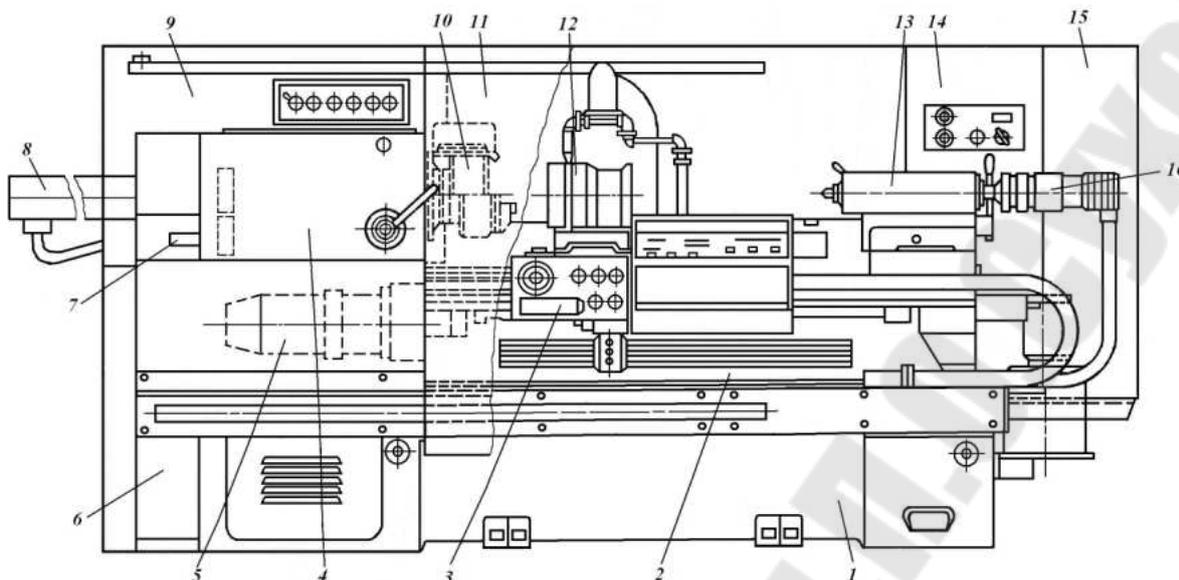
Фронтальная проекция общего вида токарно-винторезного станка с ЧПУ 16К20Т1:
